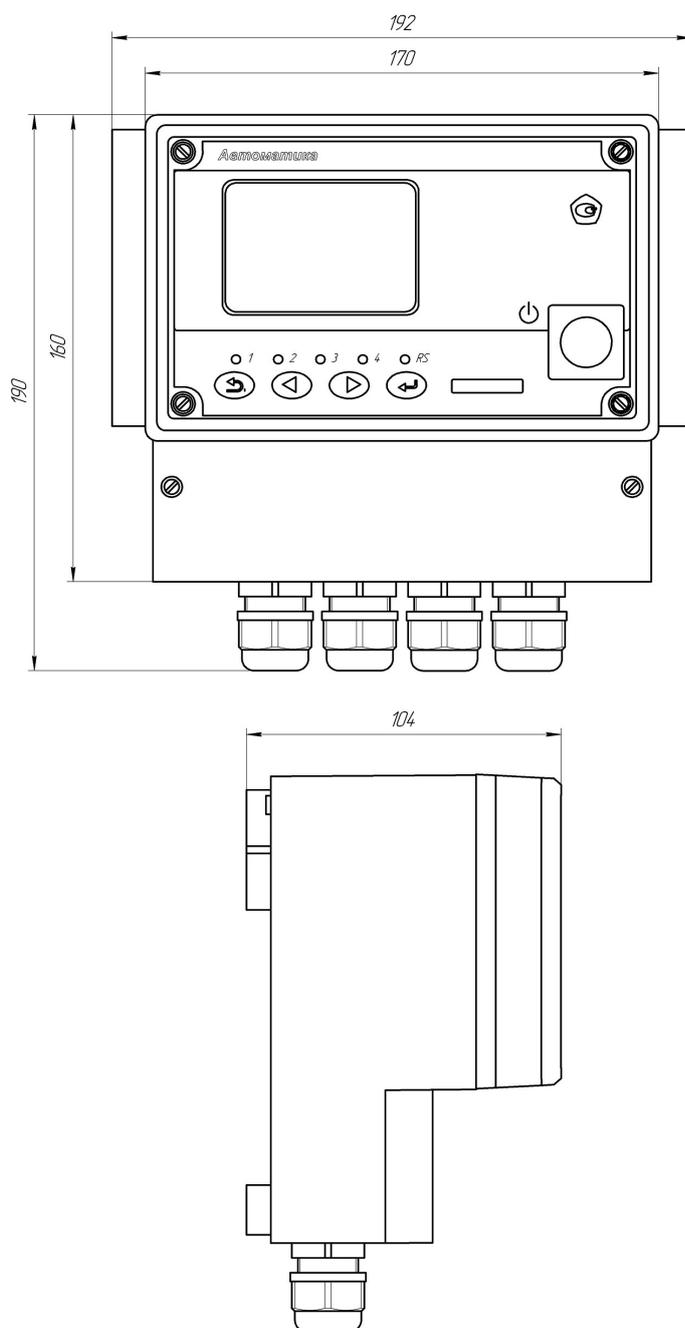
Габаритные размеры измерительного прибора АРК-5101
